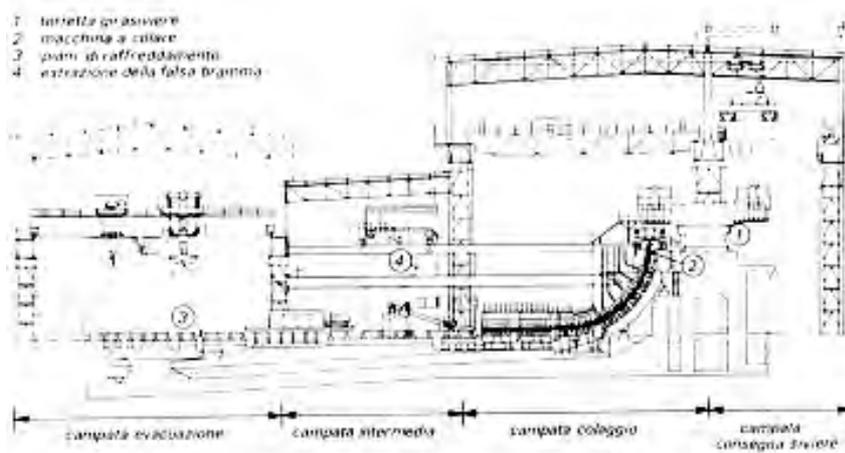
Sezione longitudinale dell'impianto di colata continua
